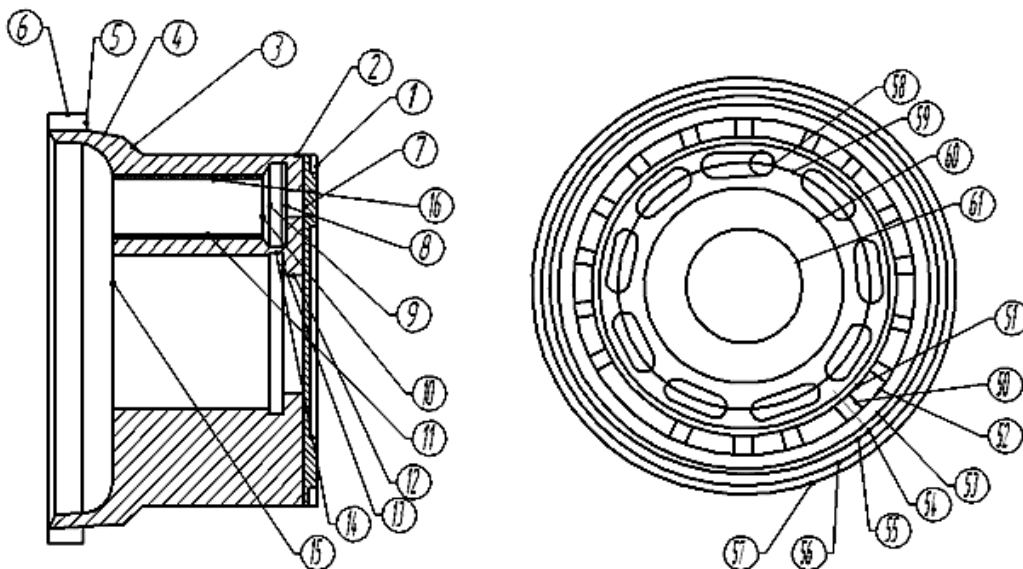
Нумерація поверхонь на корпусній деталі "Блок циліндрів"
